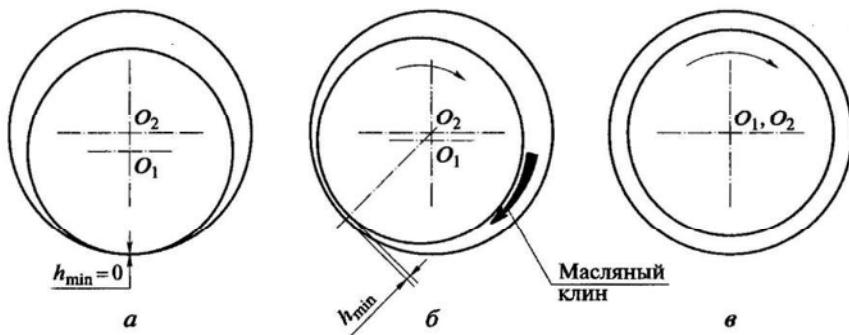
Образование масляного клина в подшипнике скольжения коленчатого вала при пуске двигателя:
